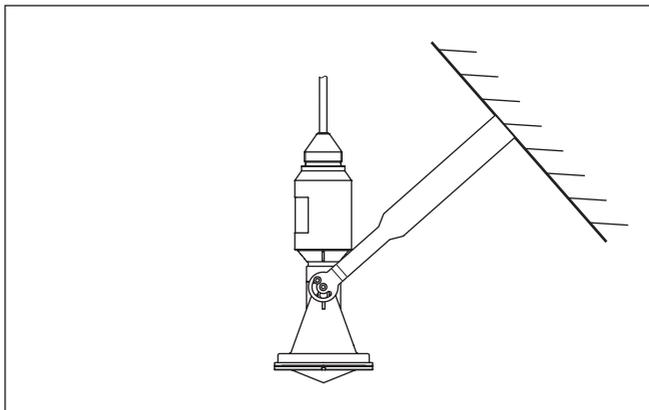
Montaggio a parete con parete inclinata tramite la staffa di montaggio lunga 300 mm
